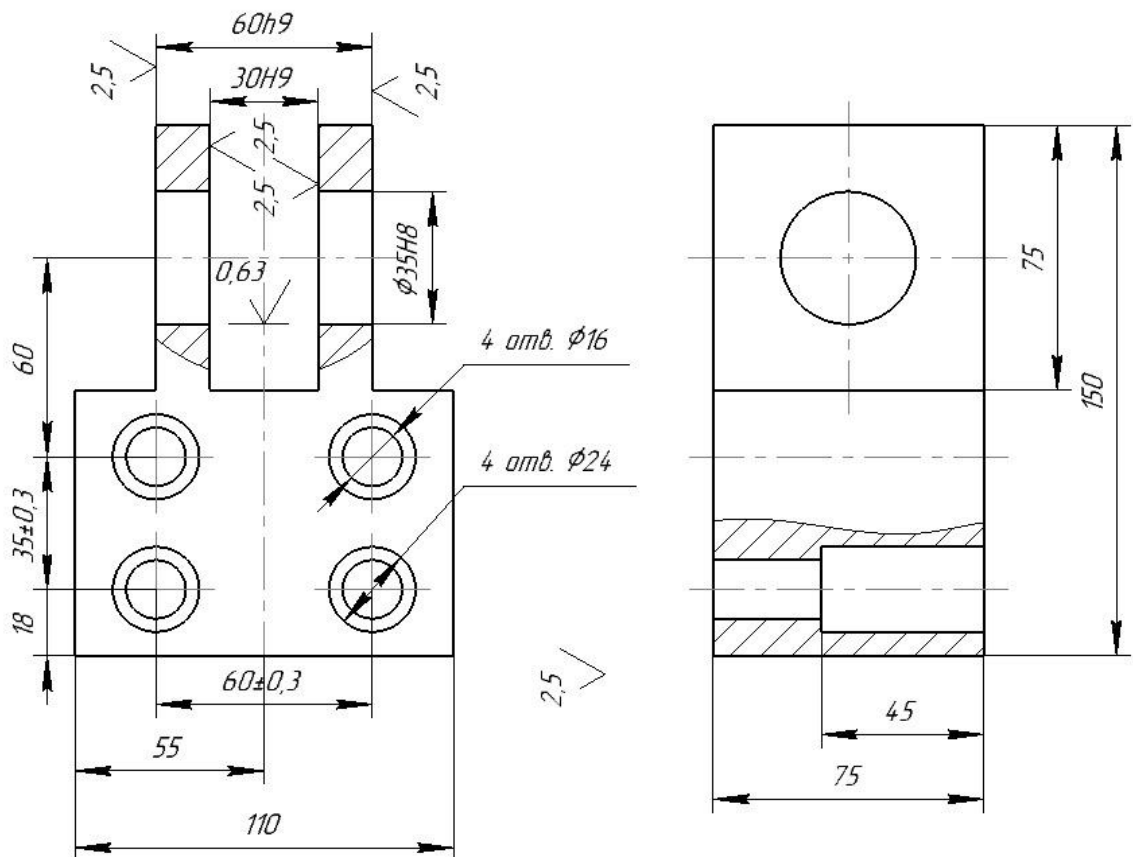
Креслення (ескіз) деталі «Вилка»
